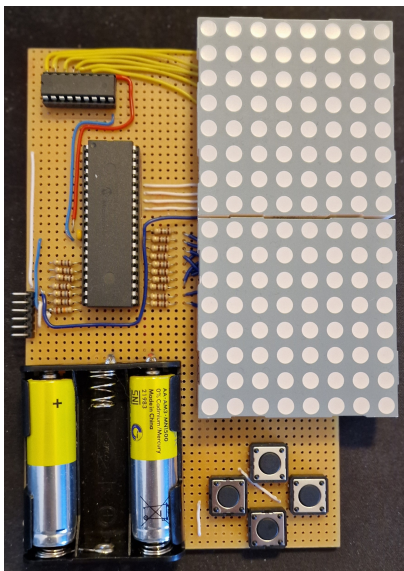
Foto van de voorkant van de Tetris gameboy, vóór de (meeste) bedradingen.
